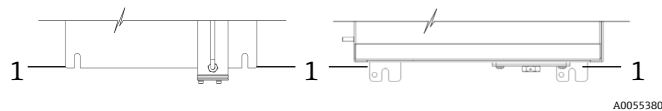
Расположение выступов с прорезями (1) для установки анализатора J22 на панель (слева) или в корпус (справа)
